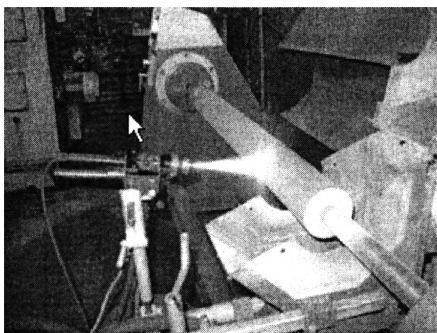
Шток-компрессора ОАО «Нафтан» – покрытие «Черный корунд»
